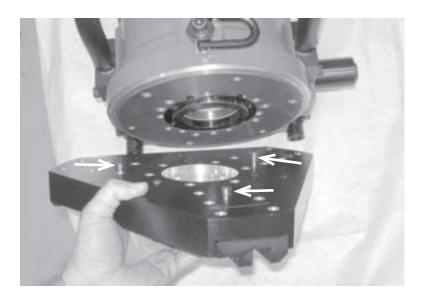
Lösen Sie die Stellschrauben, mit denen die Auslöserbaugruppe am Gehäuse befestigt ist.
